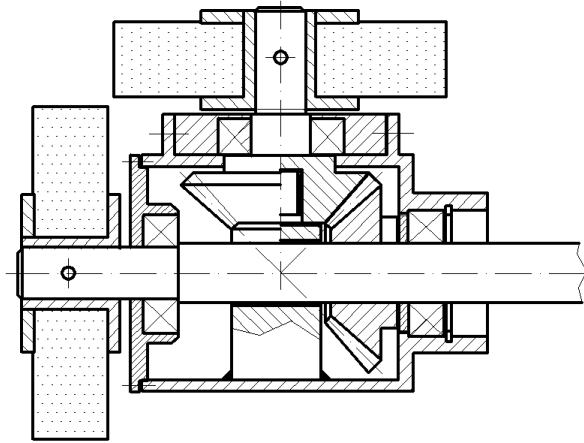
Конструкция шлифовальной головки с двумя абразивными кругами
